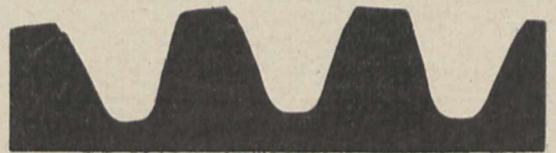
Kruppsches gehärtetes Straßenbahn-Stahlgußrad nach 175 000 Wagenkilometern, zurückgelegt im praktischen Betrieb einer Straßenbahn.
